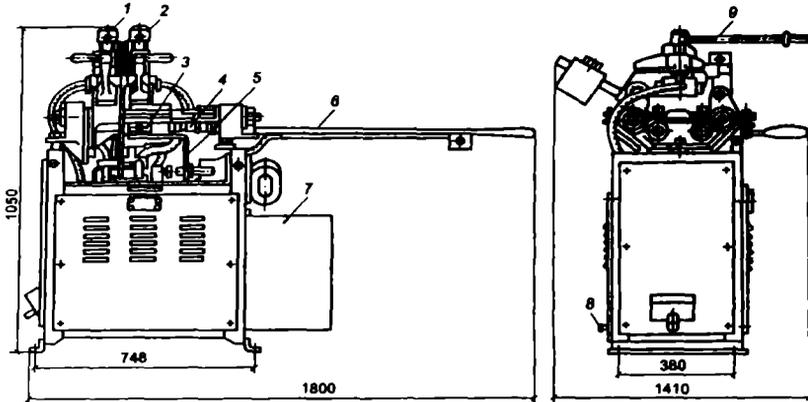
Машина MC-1602 (MCP-100) для стыковой сварки:
